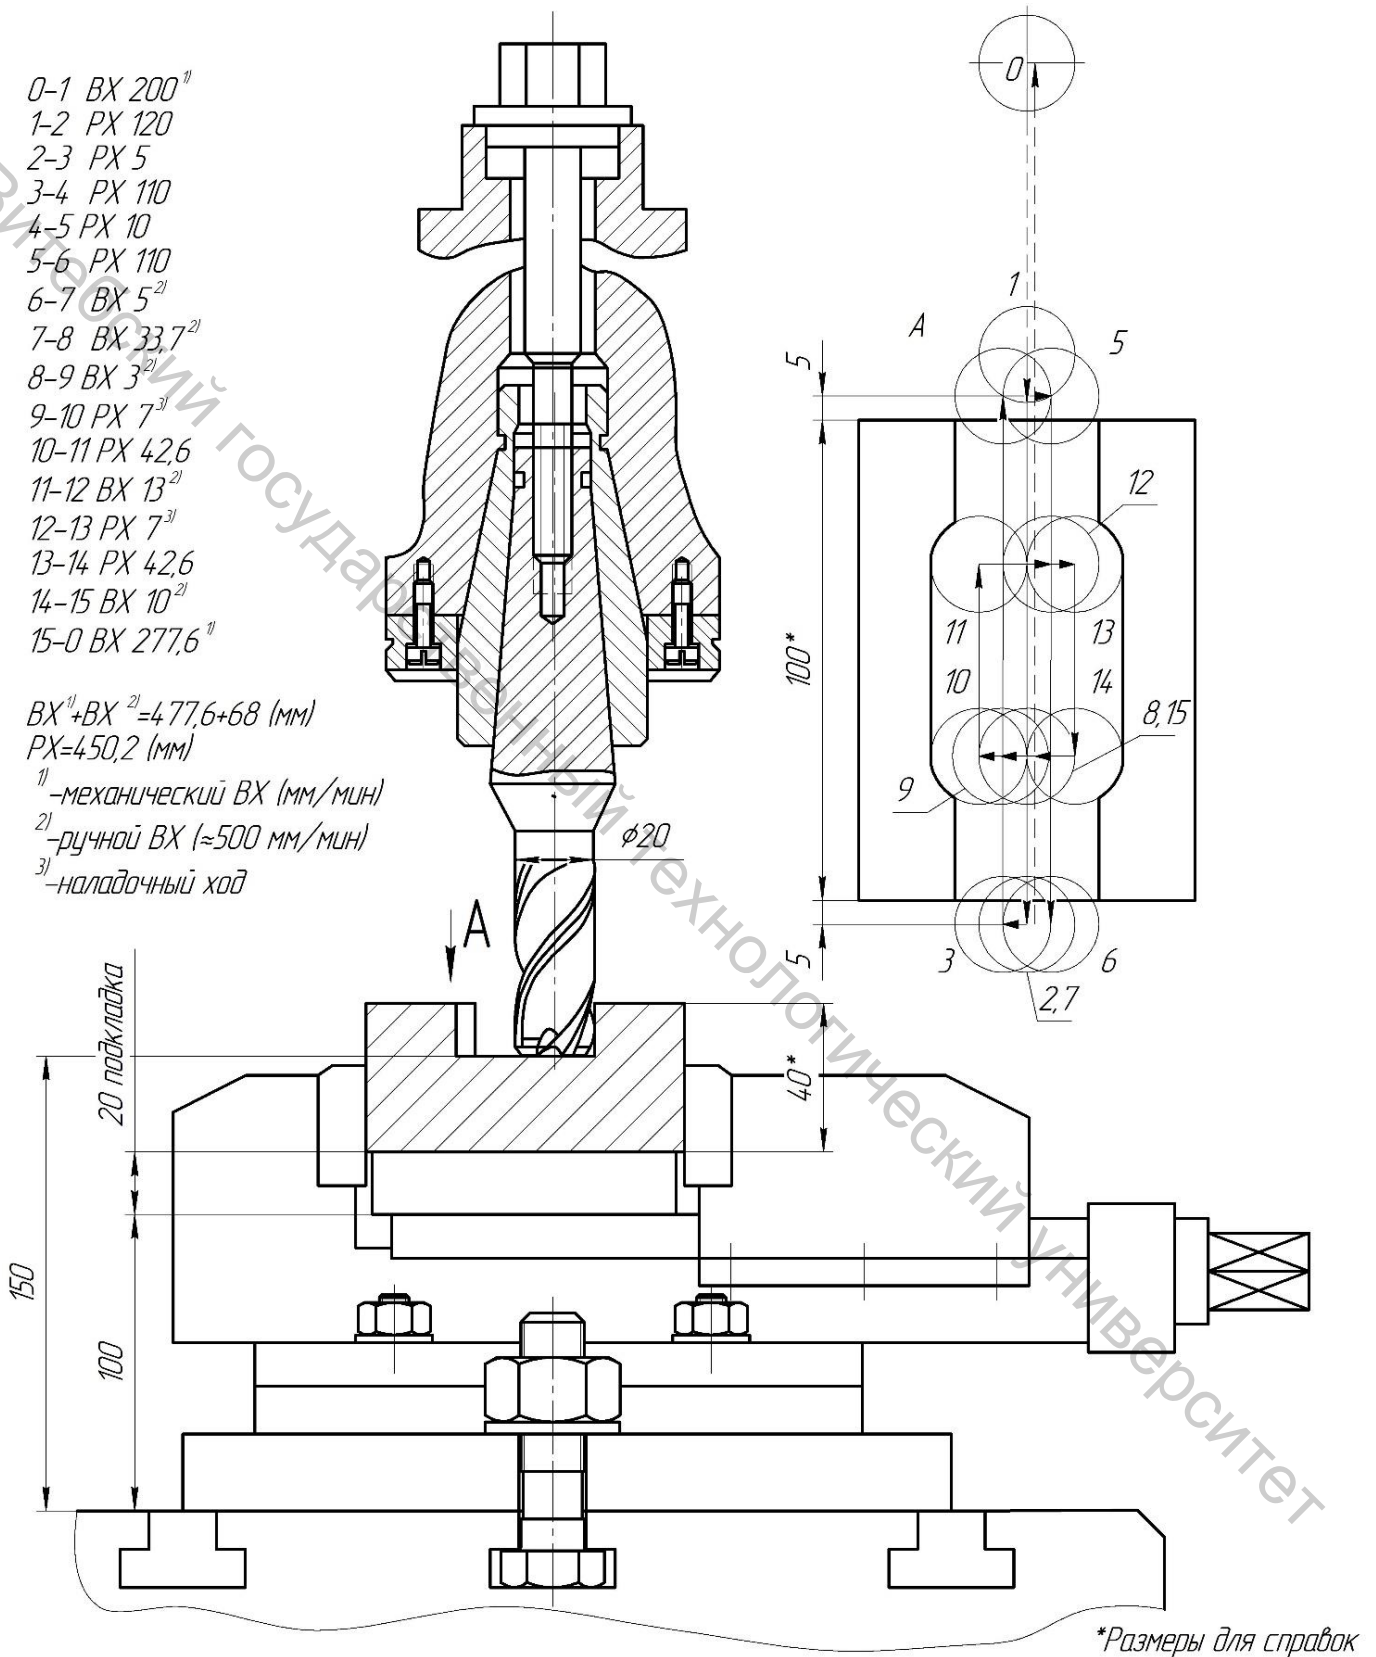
Схема наладки фрезерного станка модели 6P12 на обработку заготовки детали «Плита» (BX – вспомогательный ход, PX – рабочий ход)
